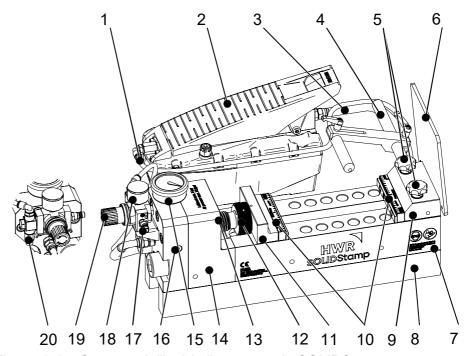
Struttura dell'unità di stampaggio SOLIDStamp
